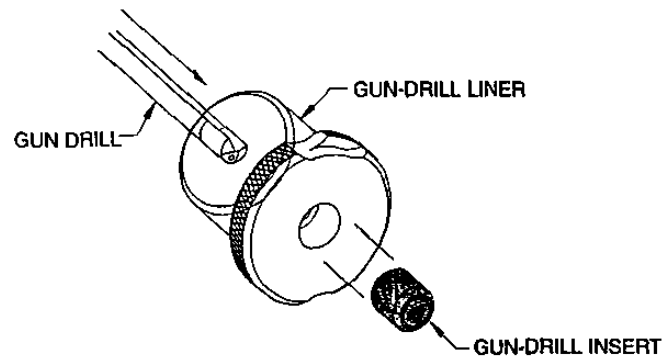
El forro de la pistola-perforadora y la pistola-perforadora que inserta los casquillos se utilizan juntos.
